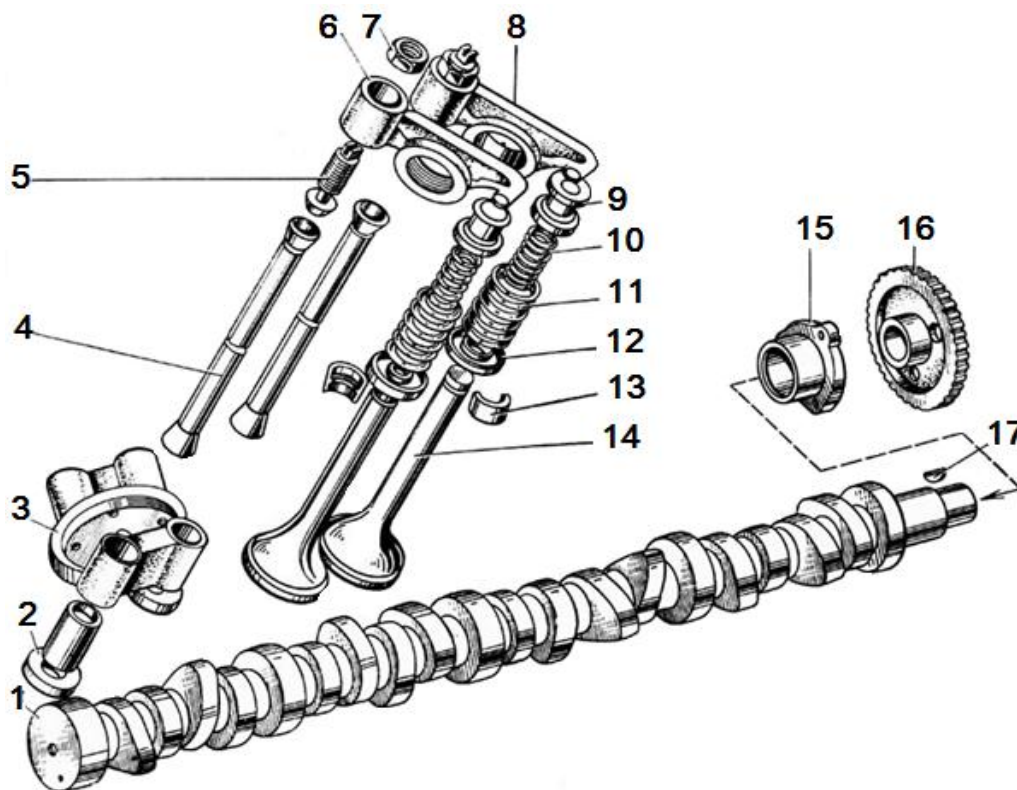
Газораспределительный механизм типа OHV:
